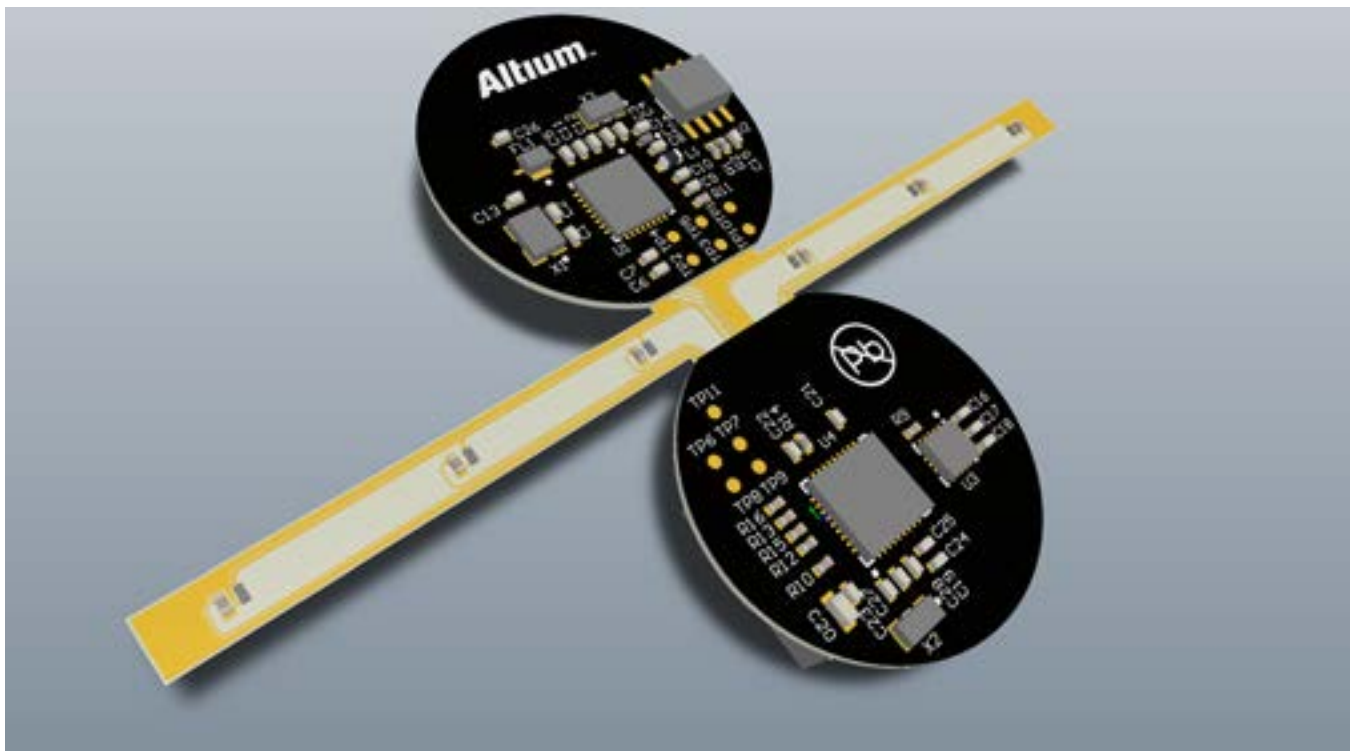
PCB-Design-Software mit 3D-Modellierung zeigt Designern genau, wie die PCB-Baugruppe zusammenpasst.
